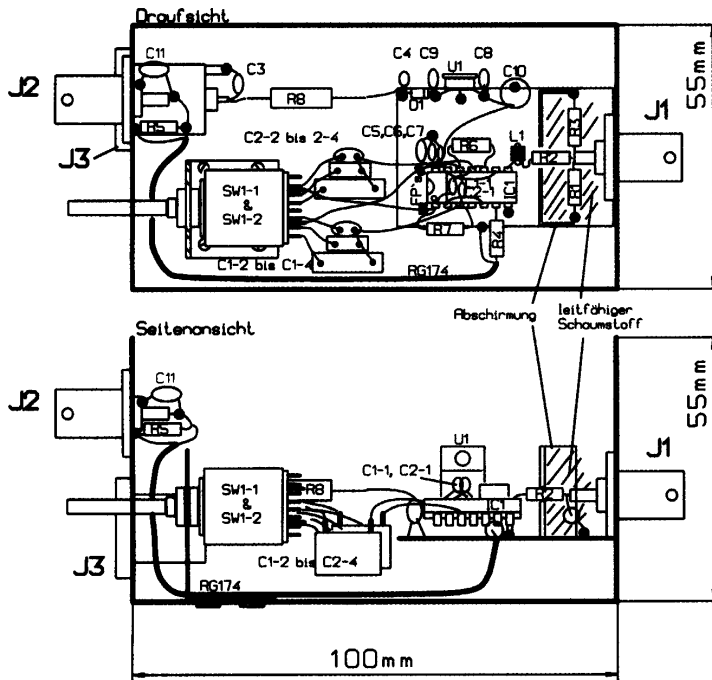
Detaillierte Aufbauzeichnung; die Platine mit der Elektronik wird von unten an die mit vier Senkschrauben und Muttern befestigte Ausgangsbuchse gelötet
